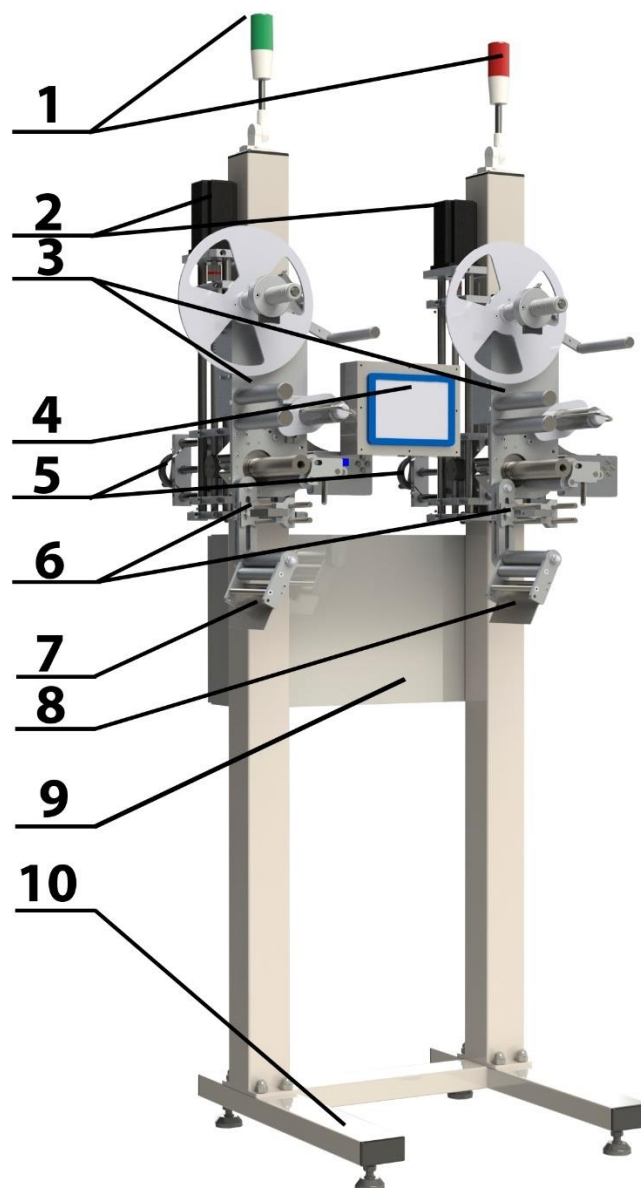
Внешний вид и обозначение основных узлов Тандема на базе Аппликаторов А-150.
